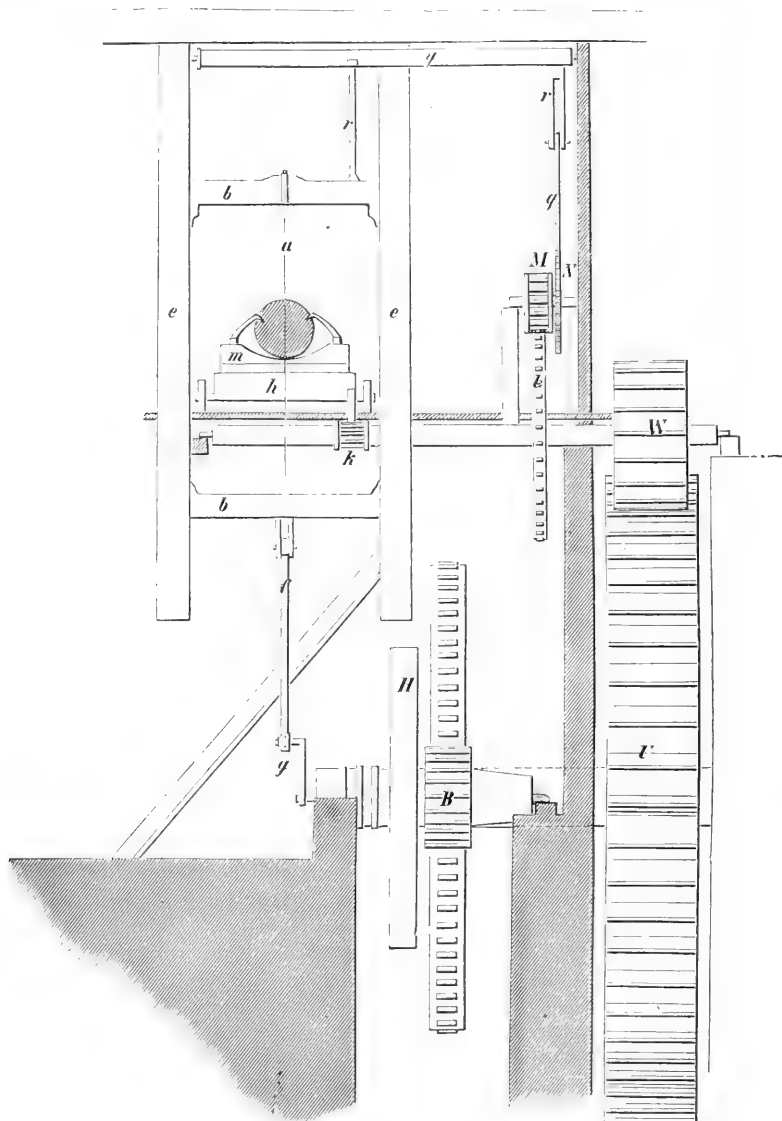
Konstruktion einer einfachen Säge mit Wasserkraftbetrieb.
